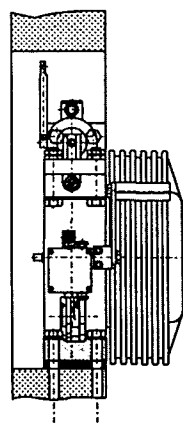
Лебедка EPM, смонтирована на поперечной балке
